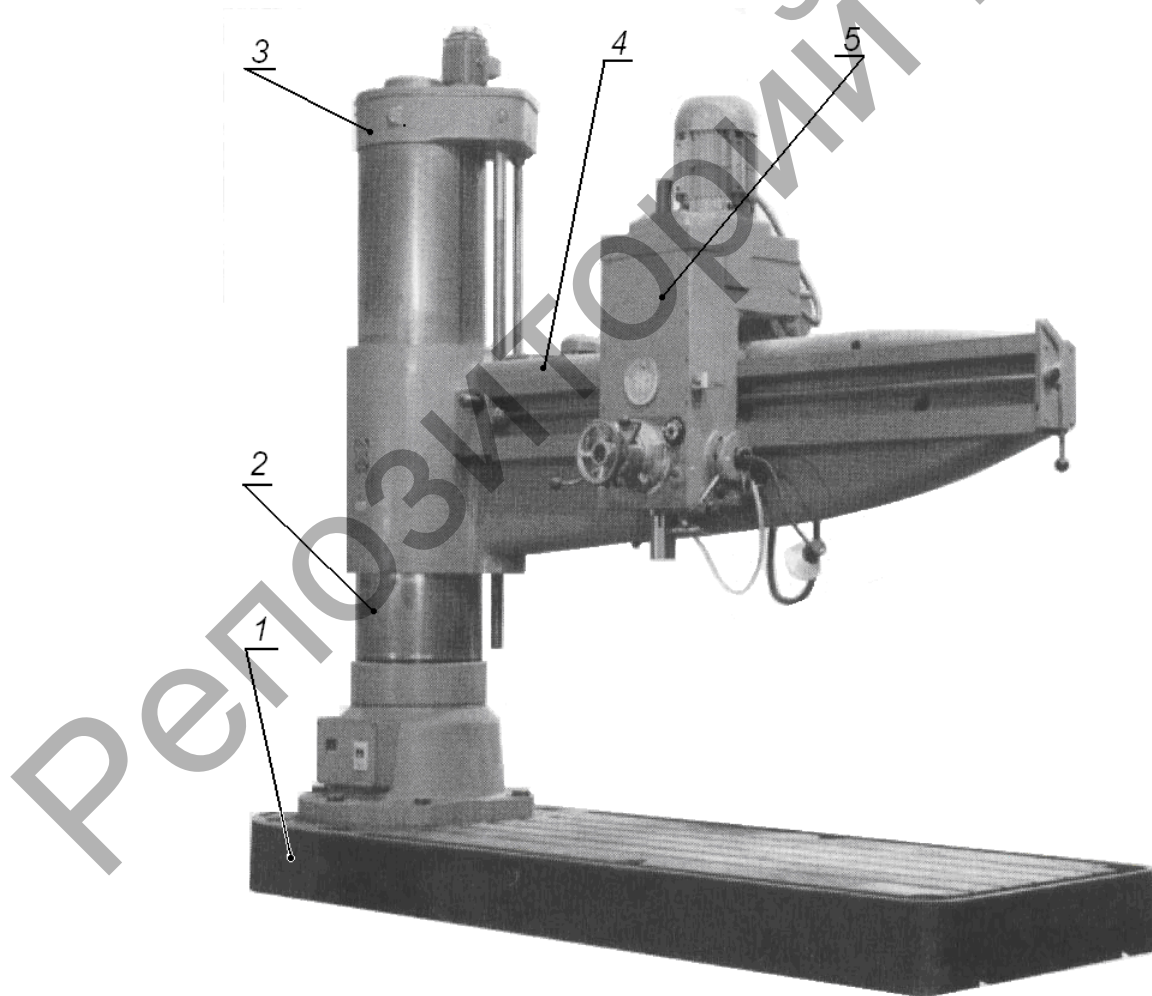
Радиально-сверлильный станок общего назначения
